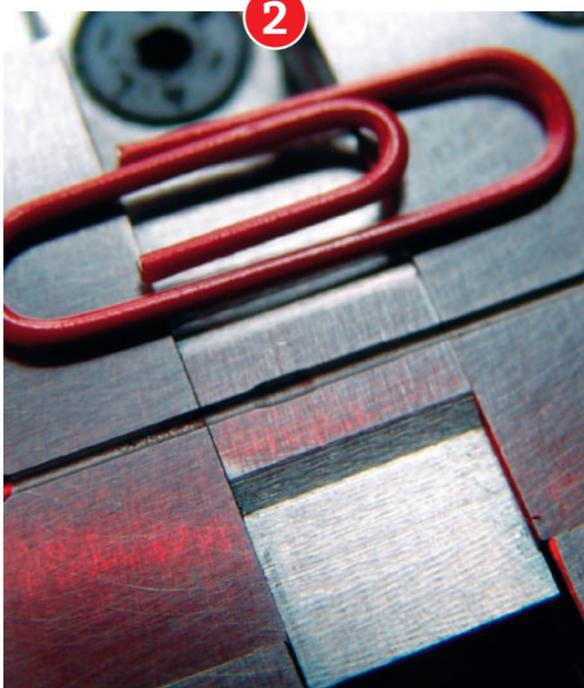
Bauteile mit einer Länge von nur wenigen Millimetern sind mit der Microhydroforming-Technik möglich. Bild: FH Köln
